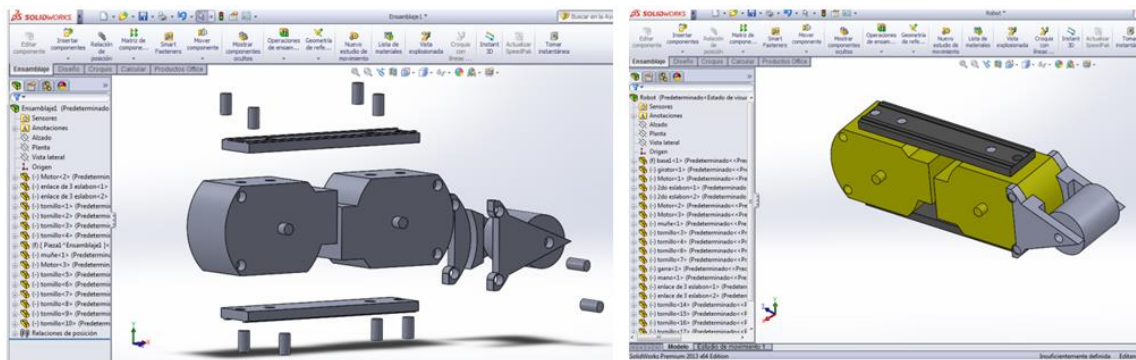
Izquierda piezas antes del ensamble, Derecha ensamble terminado y adición de apariencia (Ensamble 3).
